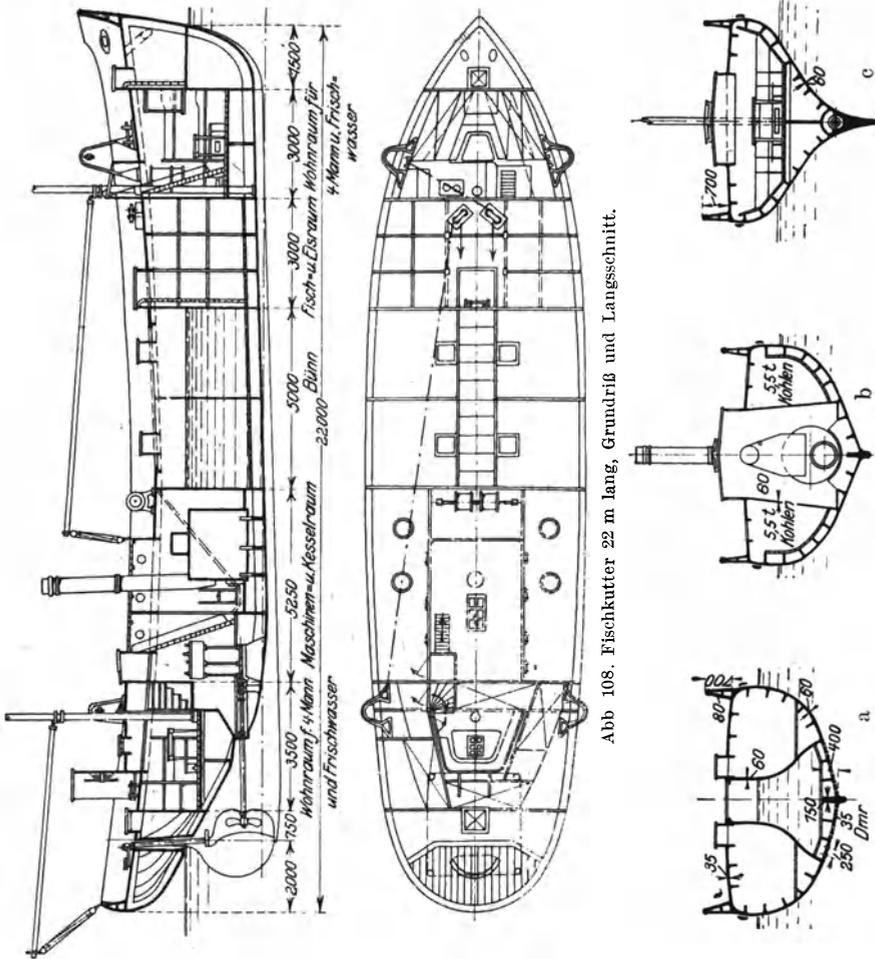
Fischkutter 22 m lang, Grundriß und Langsschnitt.
